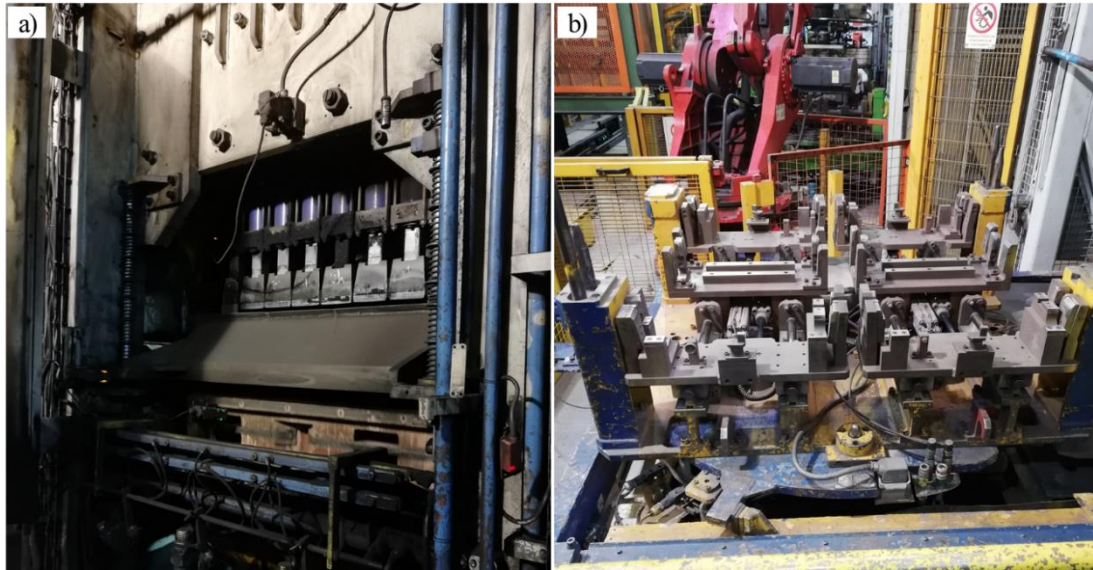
Equipamentos utilizados pela Funfrap para a preparação das moldações: a) sistema de compactação das moldações superior e inferior e b) falso-molde para colocação dos machos na moldação.
